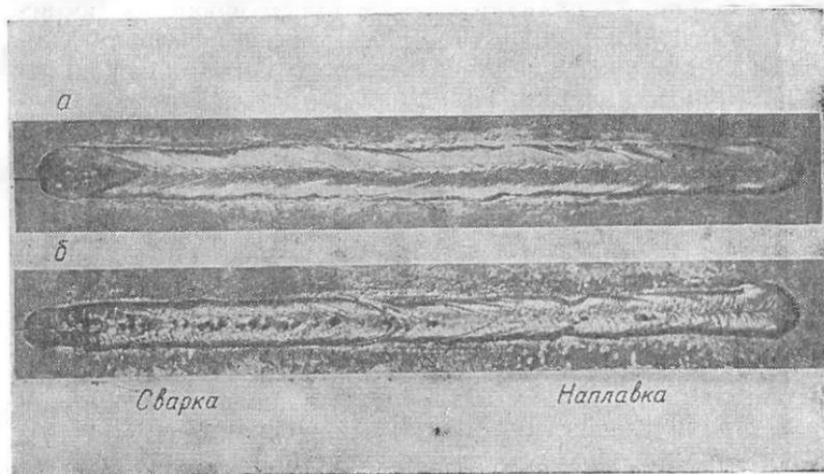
Влияние влажности флюса на пористость металла шва при автоматической сварке и наплавке на СтЗкп;
